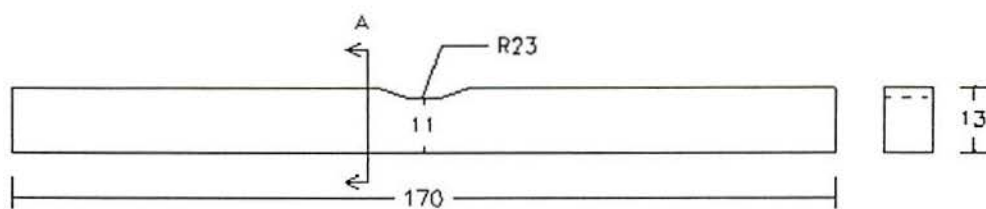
Geometria do corpo de prova Fett modificado utilizado para o ensaio em fadiga dos aços ABNT 8620N e ABNT 8650 cementados<sup>(41)</sup>, dimensões em mm.
